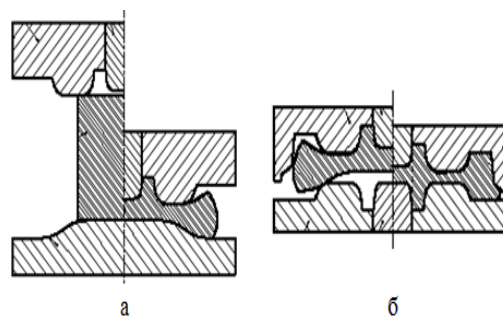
Схема черновой (а) и чистовой (б) штамповки по способу SMS EUMUCO
